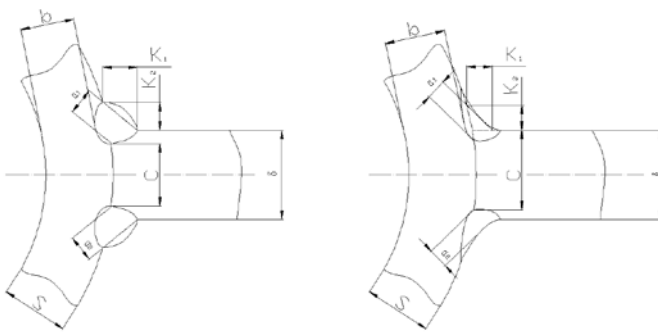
埋弧焊钢管与扁钢的焊接熔深要求
